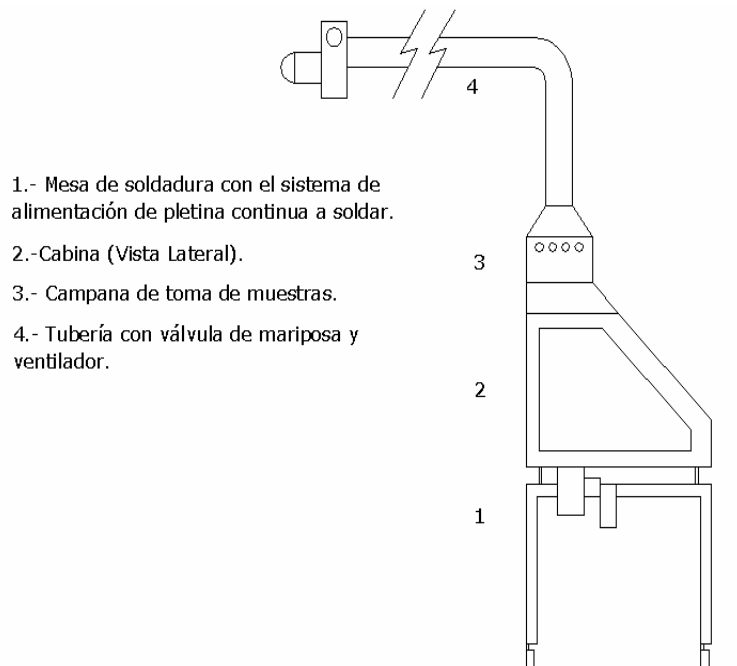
Vista general del equipo de soldadura.
